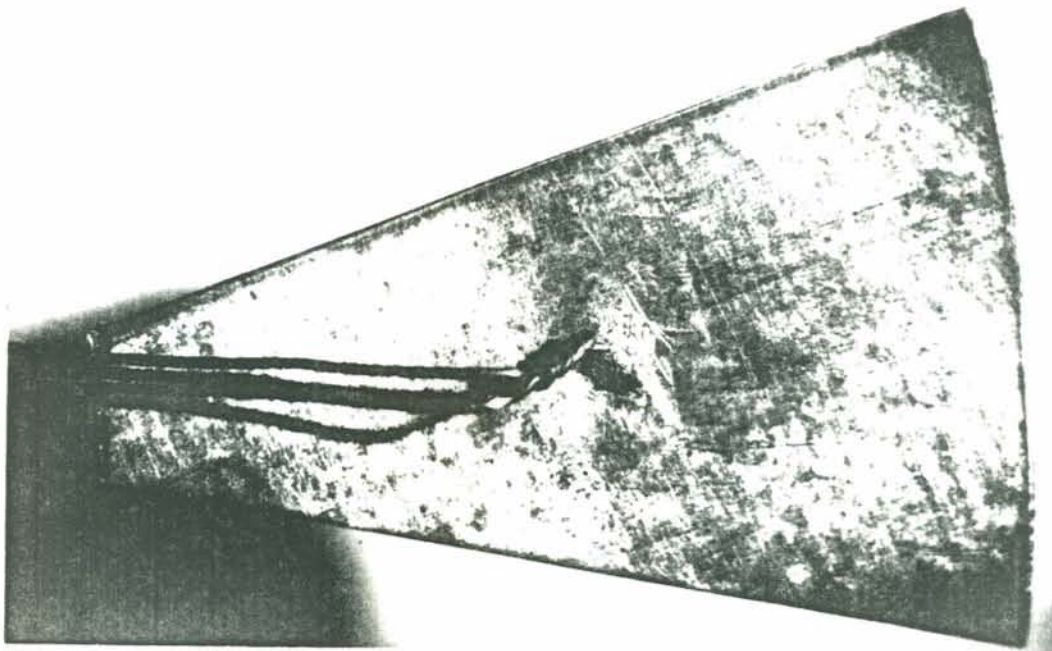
Apresentação final da solda para os elementos sensíveis confeccionados com chapas de cobre.
